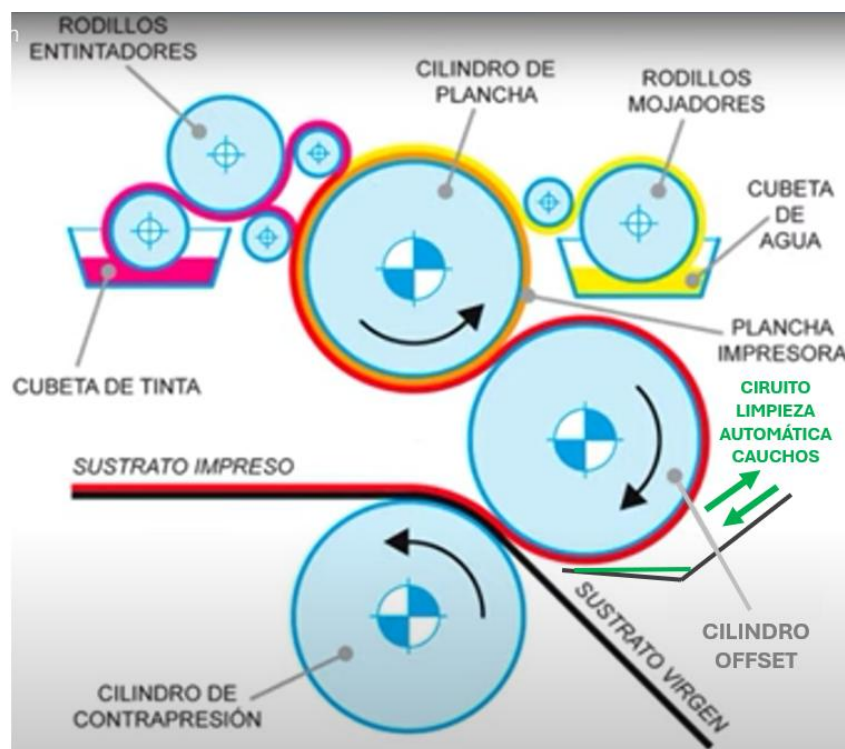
Esquema rodillos de impresión, con lavacauchos automático.
